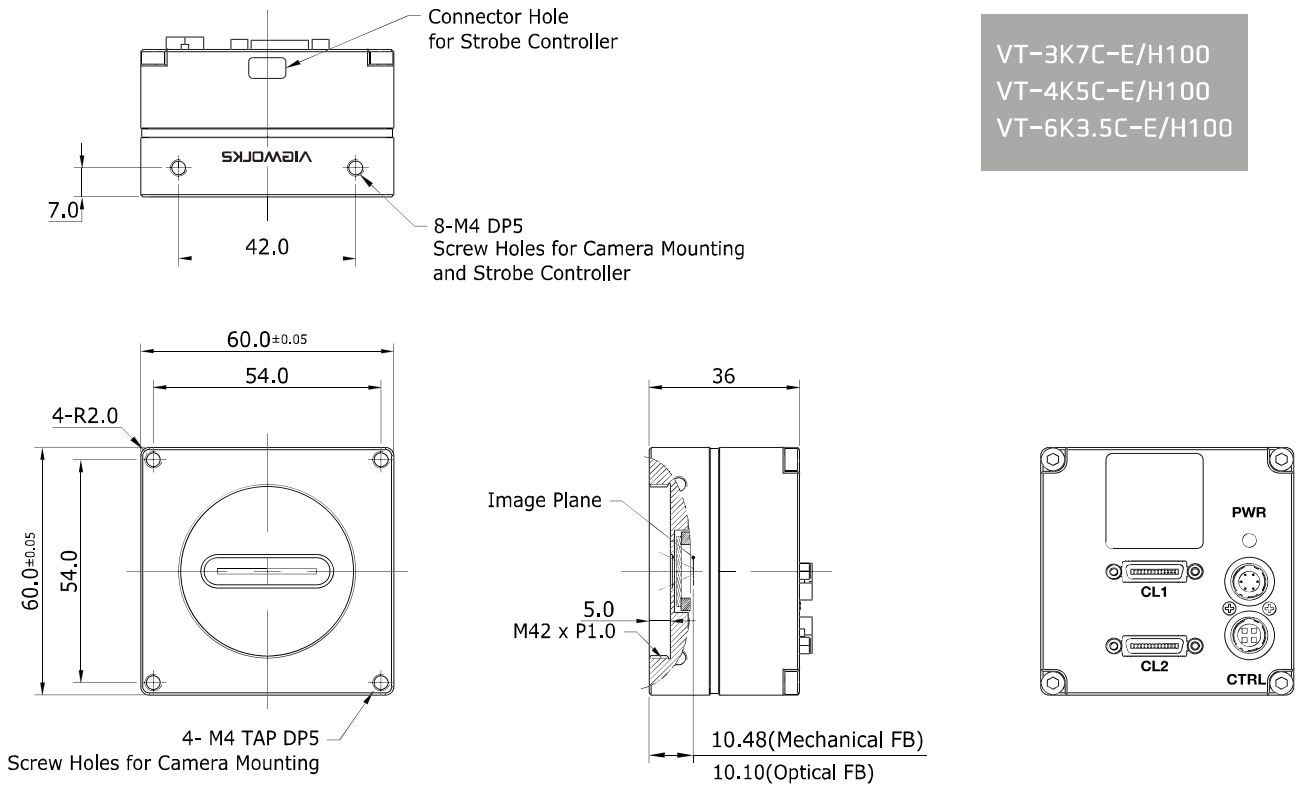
M42 mount 지원 VT CL Series Mechanical Dimension
